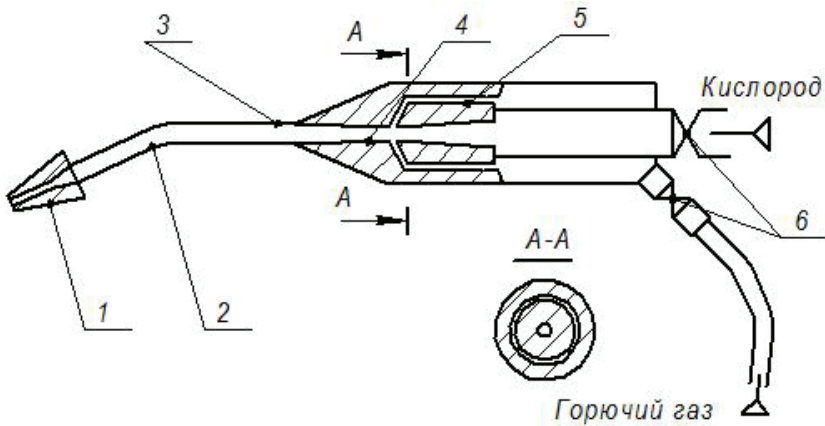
Схема газосварочной инжекторной горелки: 1 — мундштук; 2 — наконечник; 3 — камера смешения; 4 — камера; 5 — инжектор; 6 — регулировочные вентили
